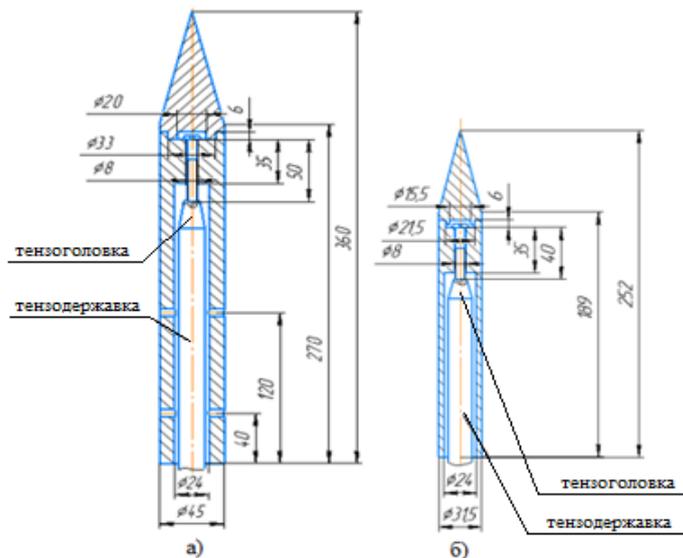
Геометрия закрепленного на весах: а – корпуса; б – ББ
